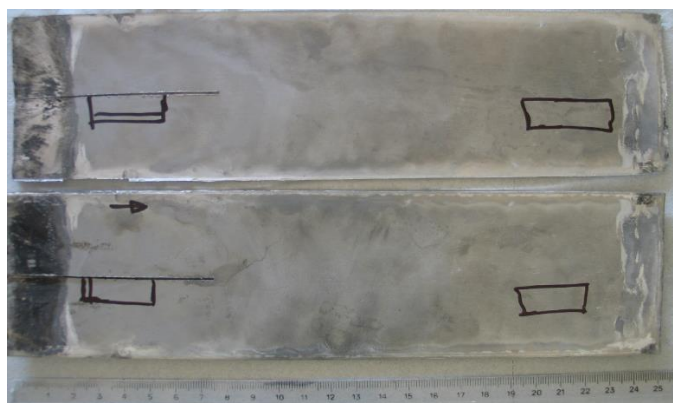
Superfície das faces que colidiram do ensaio UEW 22-Al.Fe-3.3.
